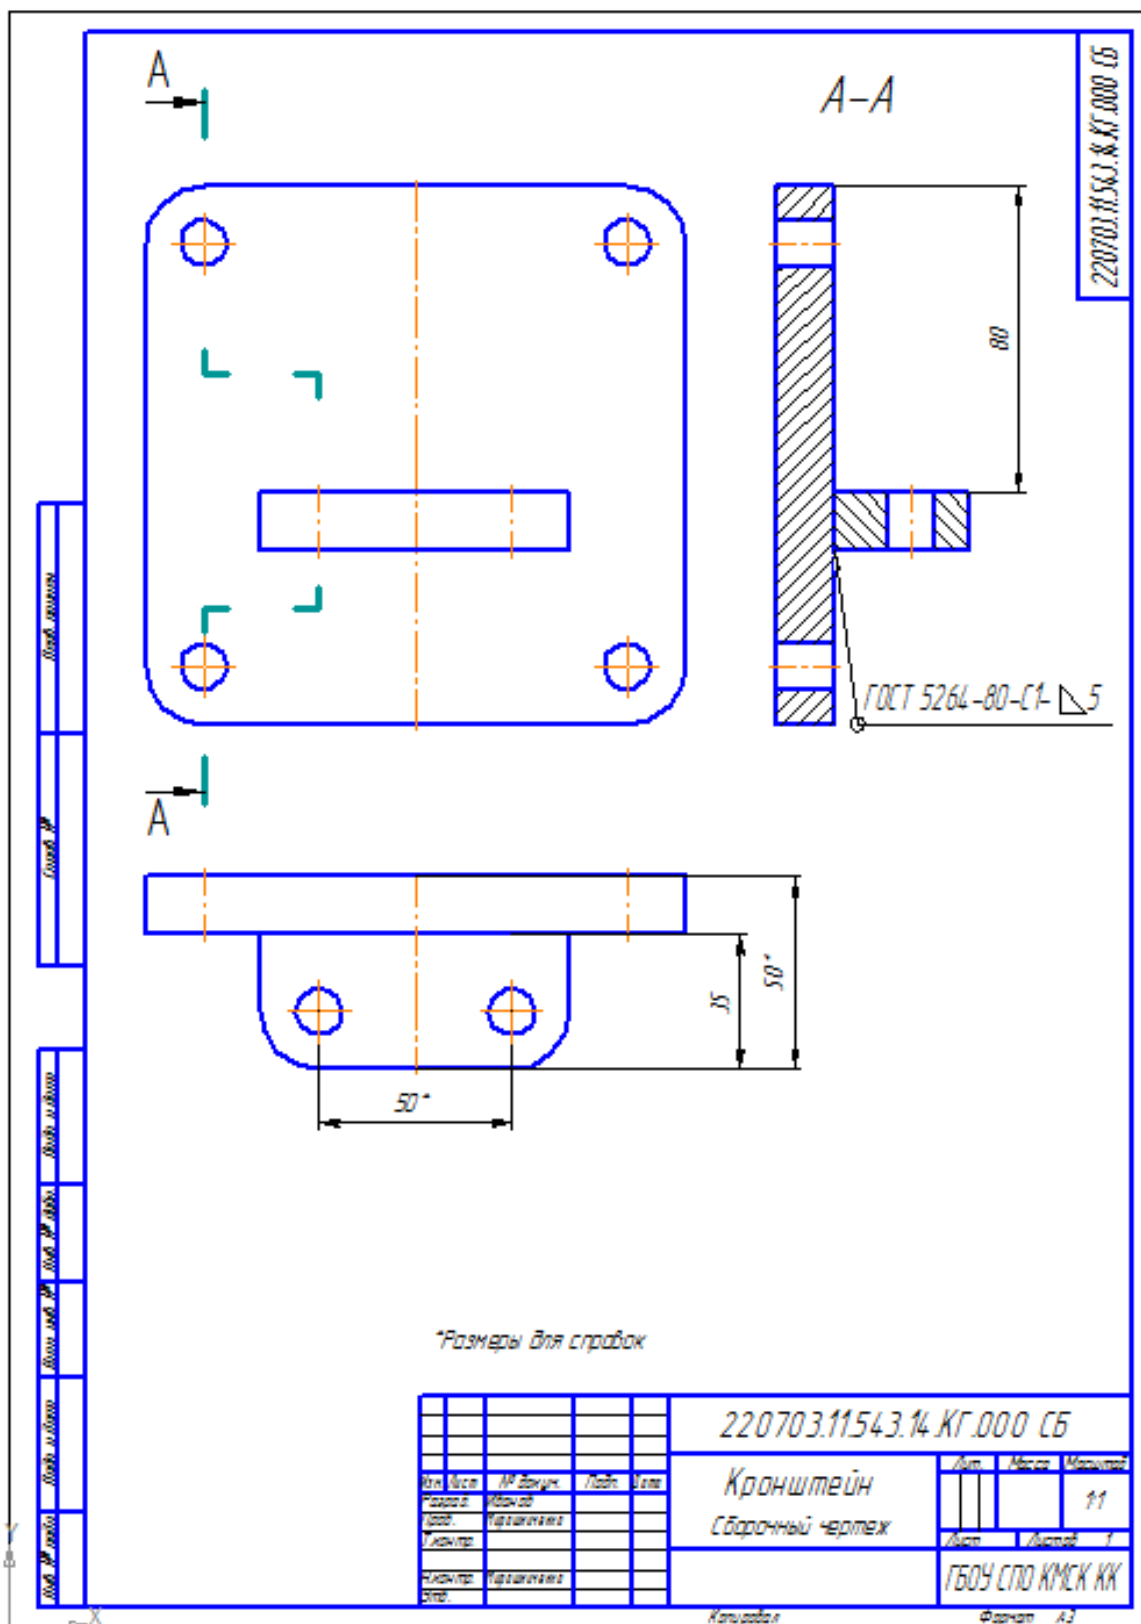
Чертеж сборочной единицы *Кронштейн
